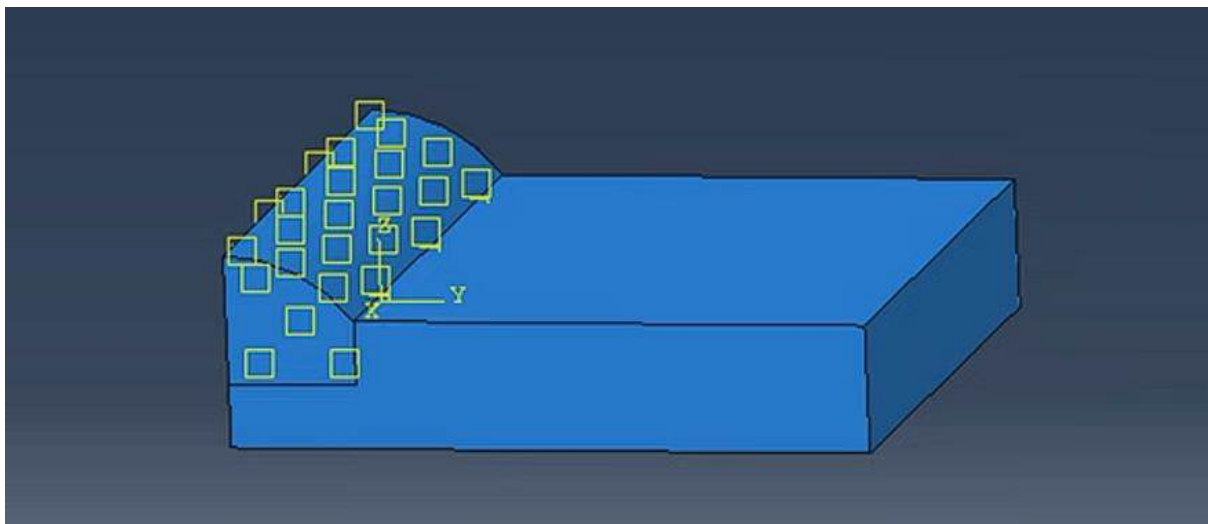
Malha 3D – Metal Base e Cordão de Solda. Fonte: Autor, 2024.
